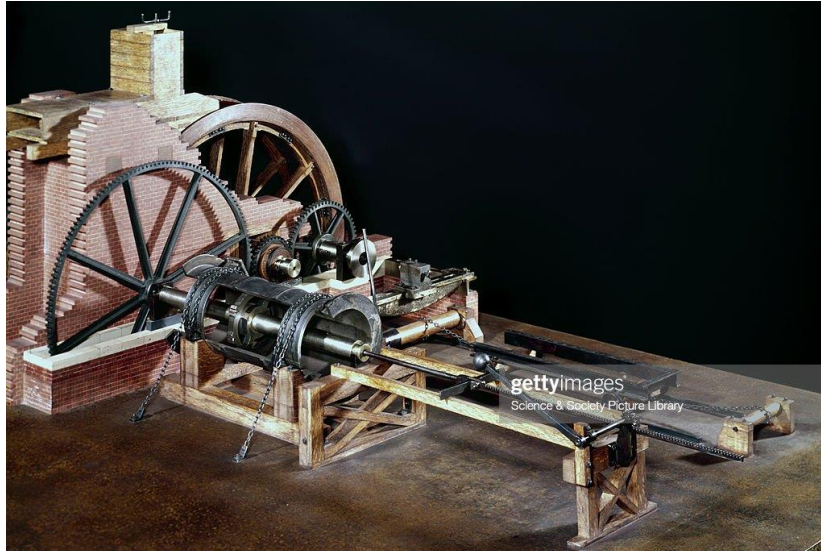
Mandrinadora horizontal de John Wilkinson (1775) accionada a rueda hidráulica. Fuente: Boring mill, Wilkinsons iron works, Bersham, nr Wrexham, Wales, 1775. www.gettyimages.ch
